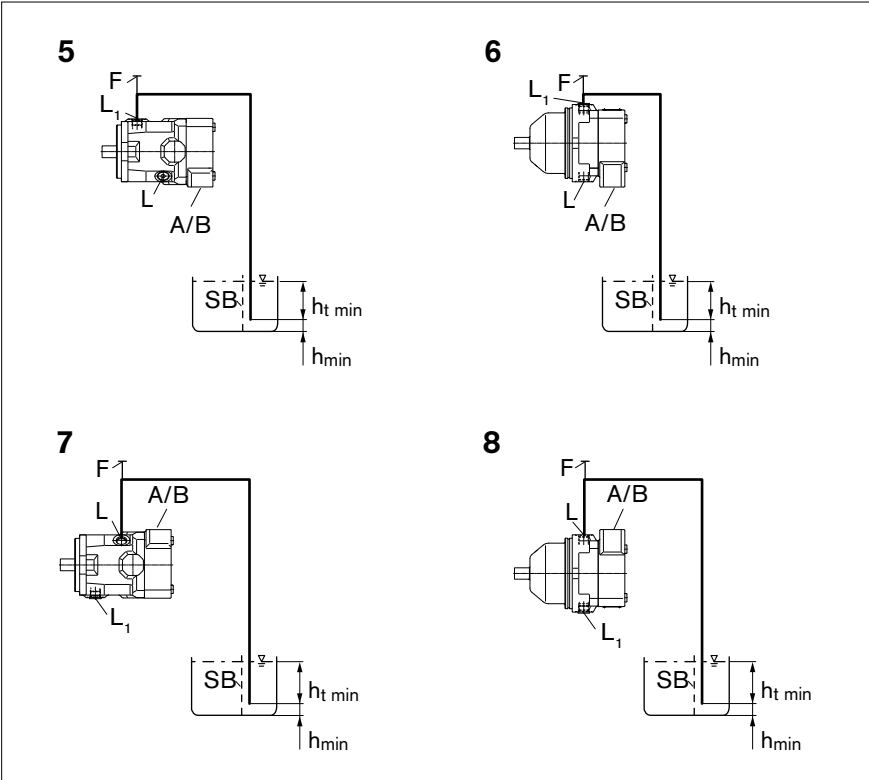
Montaggio al di sopra del serbatoio di A10FM con posizione di montaggio 5-8
